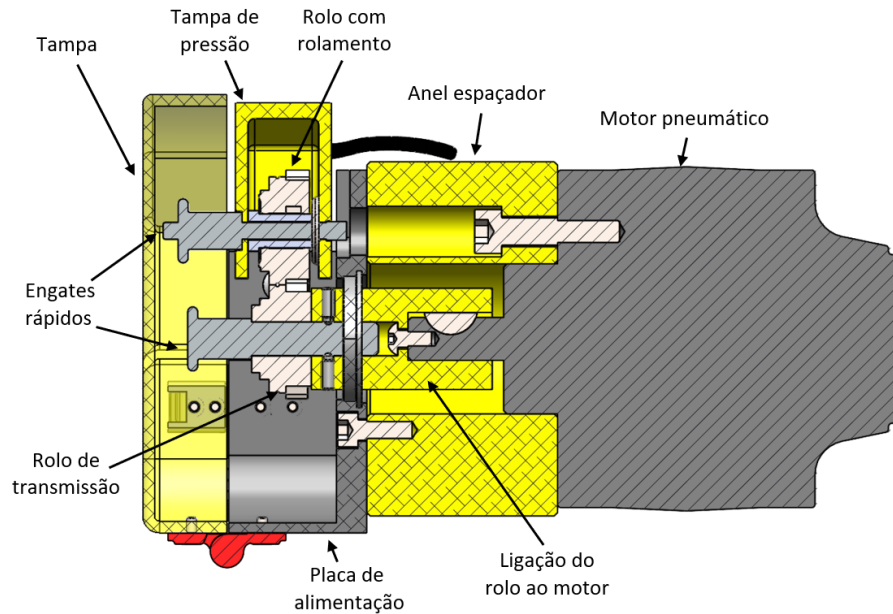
Vista em corte do sistema de alimentação de fio de soldadura
